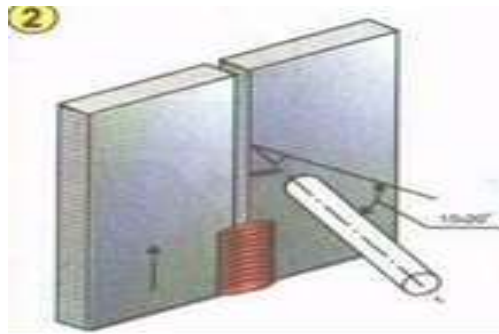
Сварка встык в вертикальном положении пластин.
